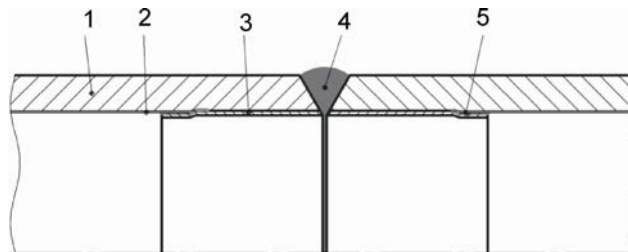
Сварное соединение труб с внутренним защитным покрытием и наконечником:
